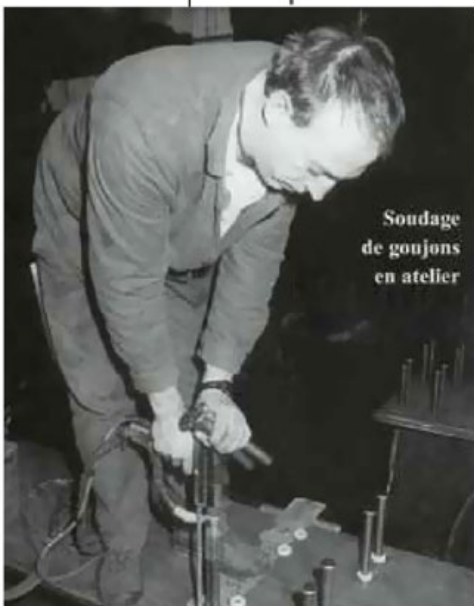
a et b : Soudage des goujons (bibliographie [6]).
